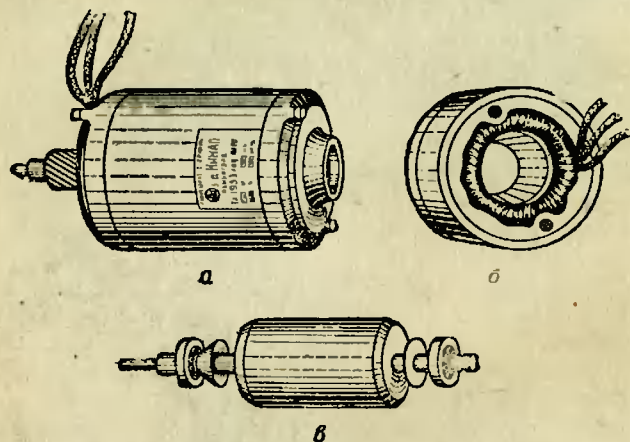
Однофазный асинхронный двигатель: а — общий вид, б — статор, в — ротор.
